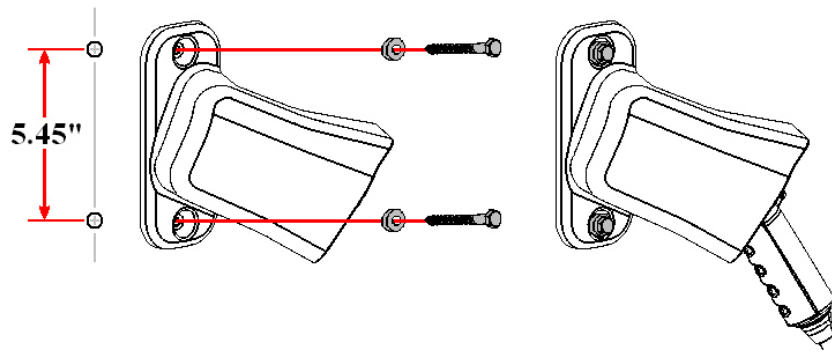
Montaje de la funda del conector SAE J1772 utilizando los tornillos y arandelas exteriores para madera
